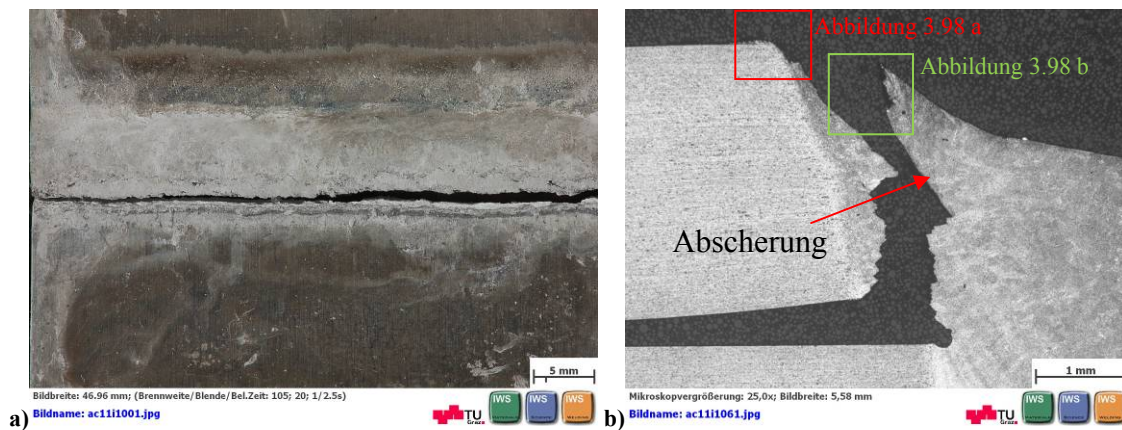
Bruchverlauf AW-5083-O in der AlMg5 Schweißnaht nach 480h NSS Test a) Draufsicht b) Querschliff
